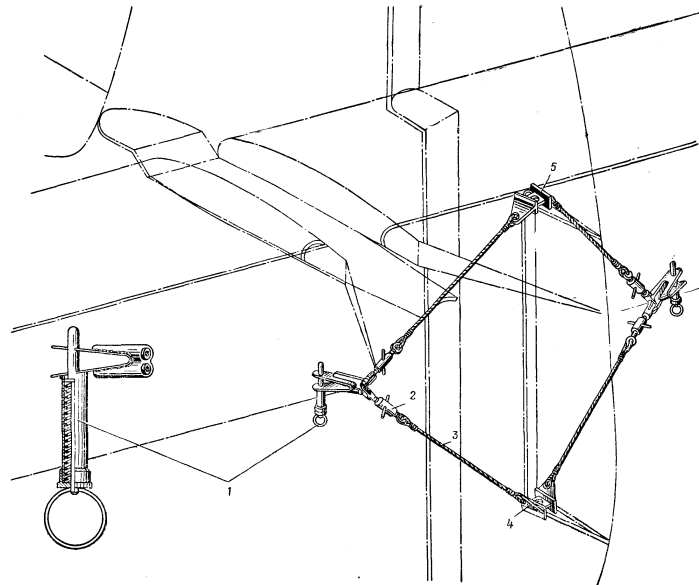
Шторовой стопор рулей высоты и направления на самолетах с № 136-0,1:
